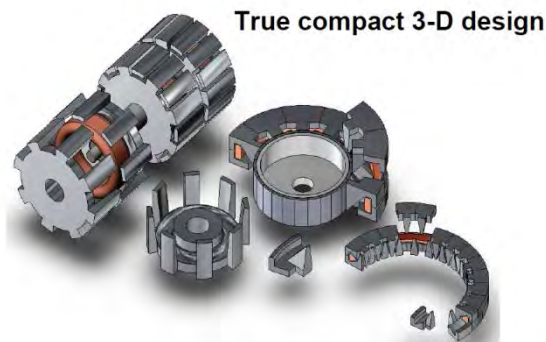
совершенствование конструкций двигателей за счет порошковых деталей, формирующих трехмерные магнитные потоки
